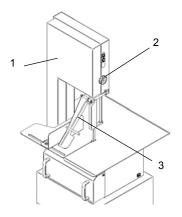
Posicionar el interruptor diferencial que está instalado arriba de la máquina, en la posición "I".
